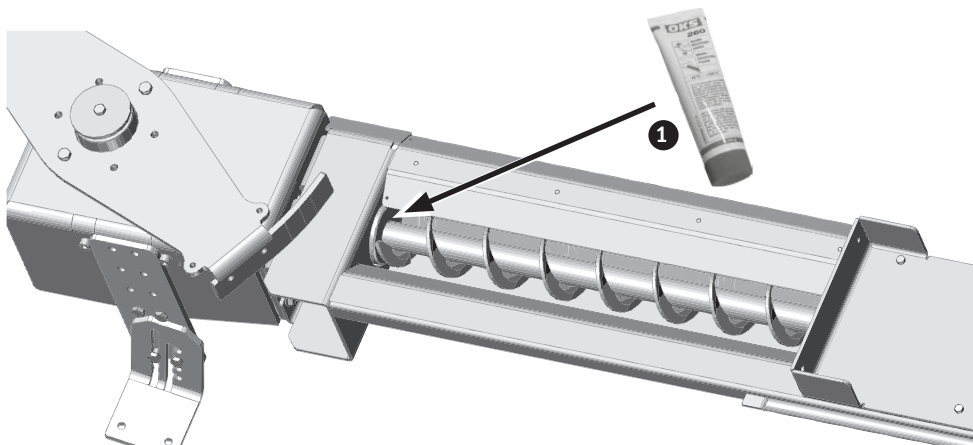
Schnecke mit dem Rührwerk-Getriebe verbinden
